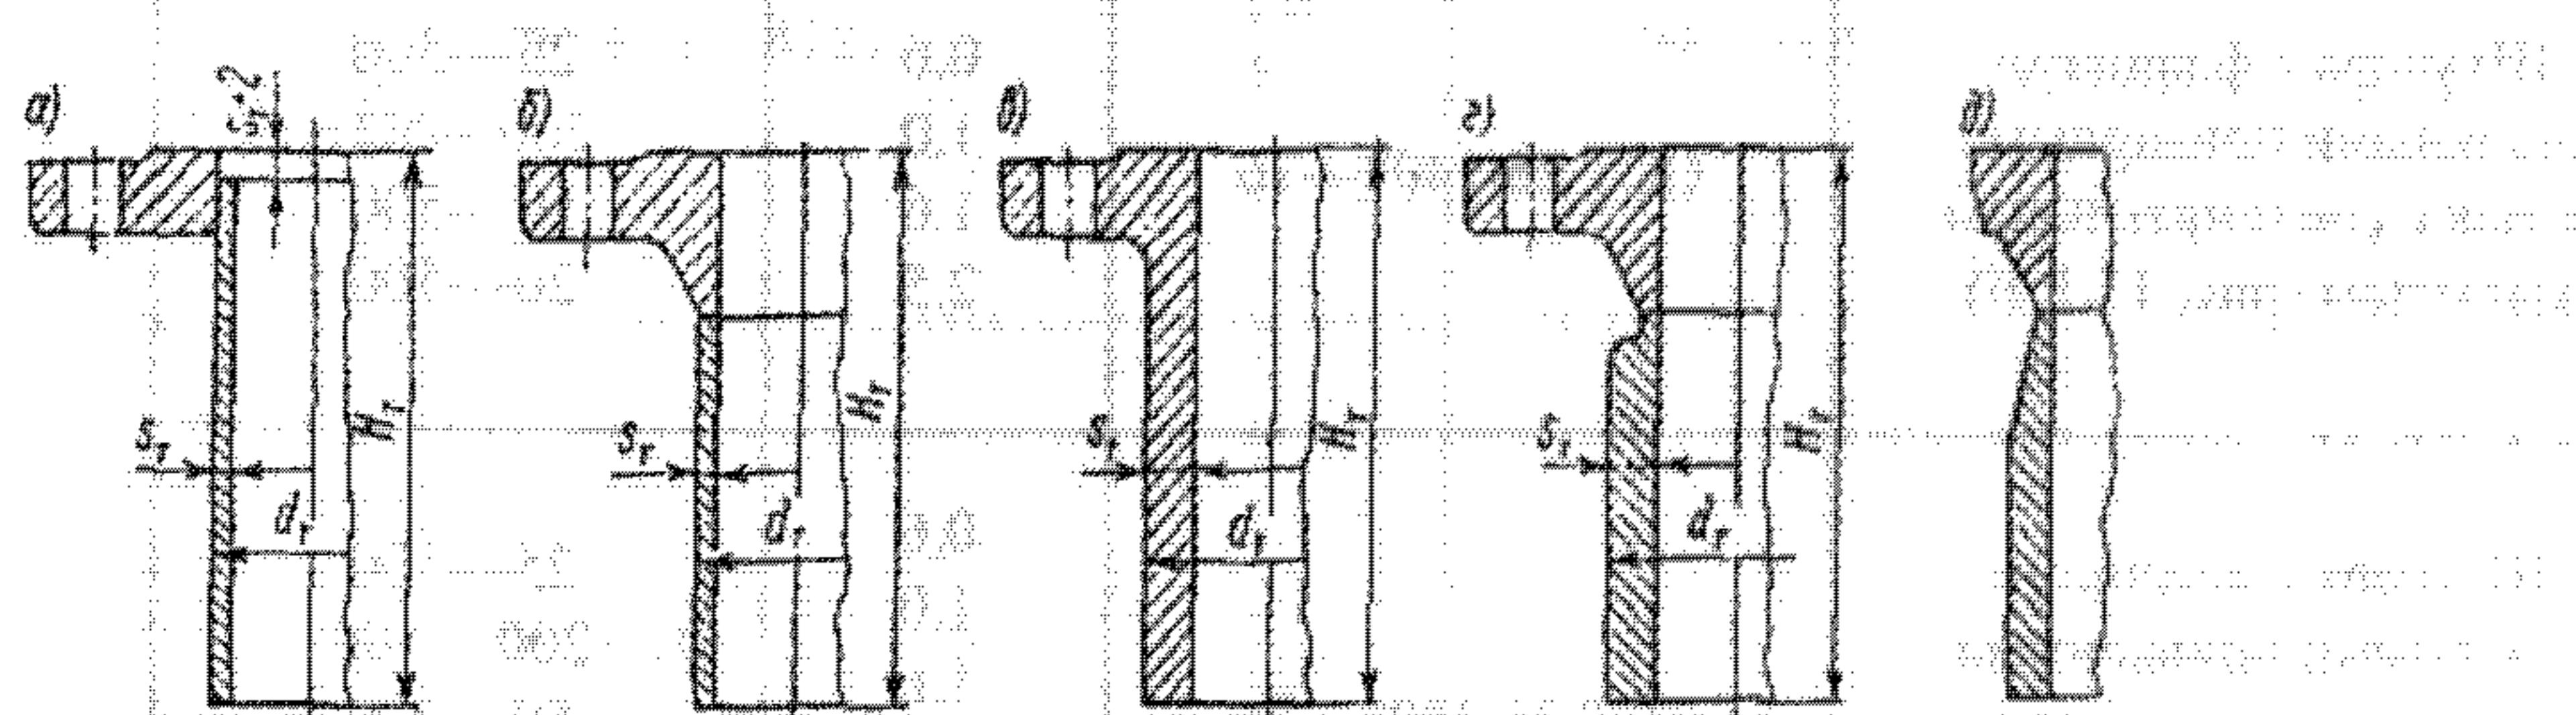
Конструкции стандартных стальных приварных фланцевых штуцеров: *а* — с приварным плоским фланцем и тонкостенным патрубком; *б* — с приварным фланцем встык и тонкостенным патрубком; *в* — кованый толстостенный; *г* — с приварным фланцем встык и толстостенным патрубком; *д* — вариант конструкции сварного толстостенного штуцера
